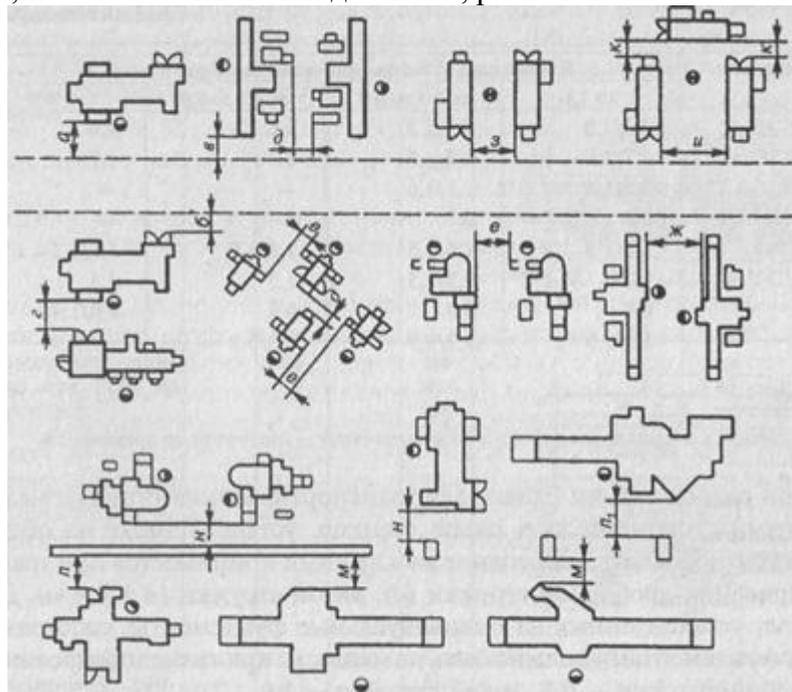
Варианты размещения станков от проездов, относительно друг друга, от стен и колонн здания
